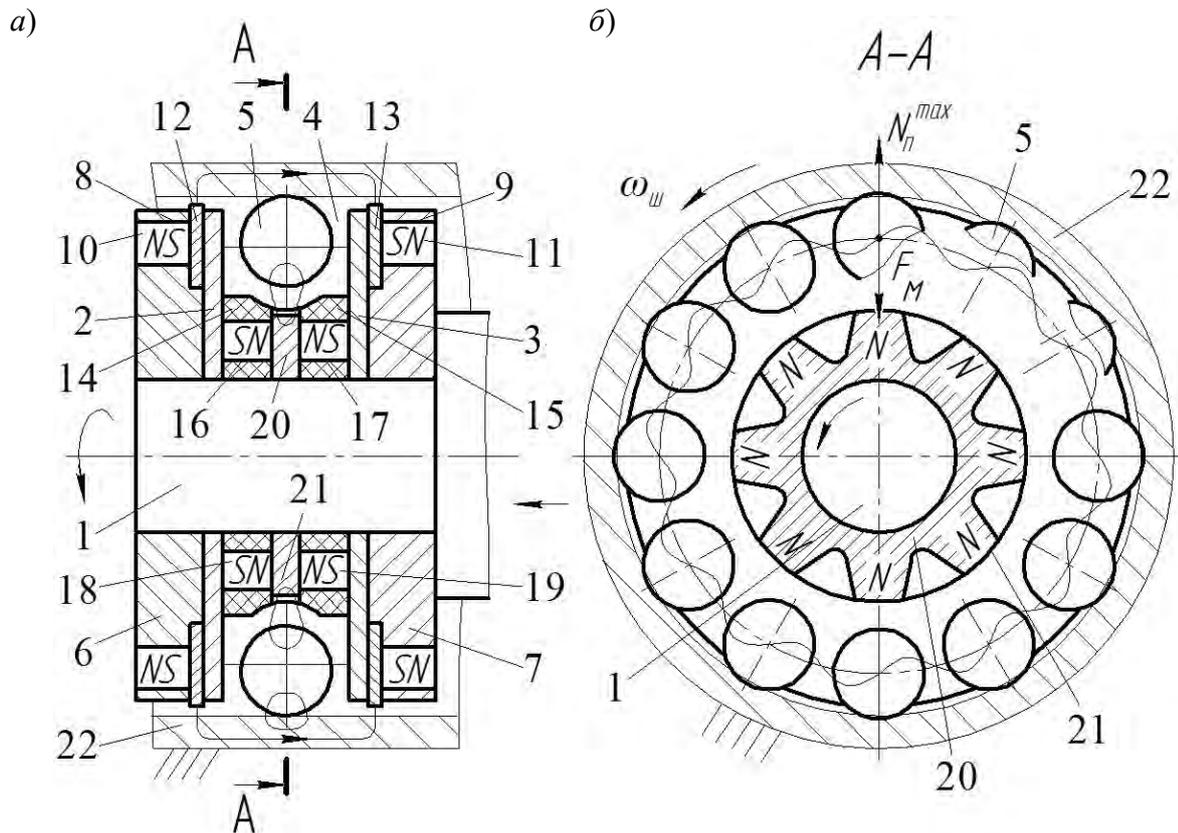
Комбинированный инструмент для СМДО внутренней цилиндрической поверхности ферромагнитных деталей: *а* – общий вид; *б* – поперечное сечение
